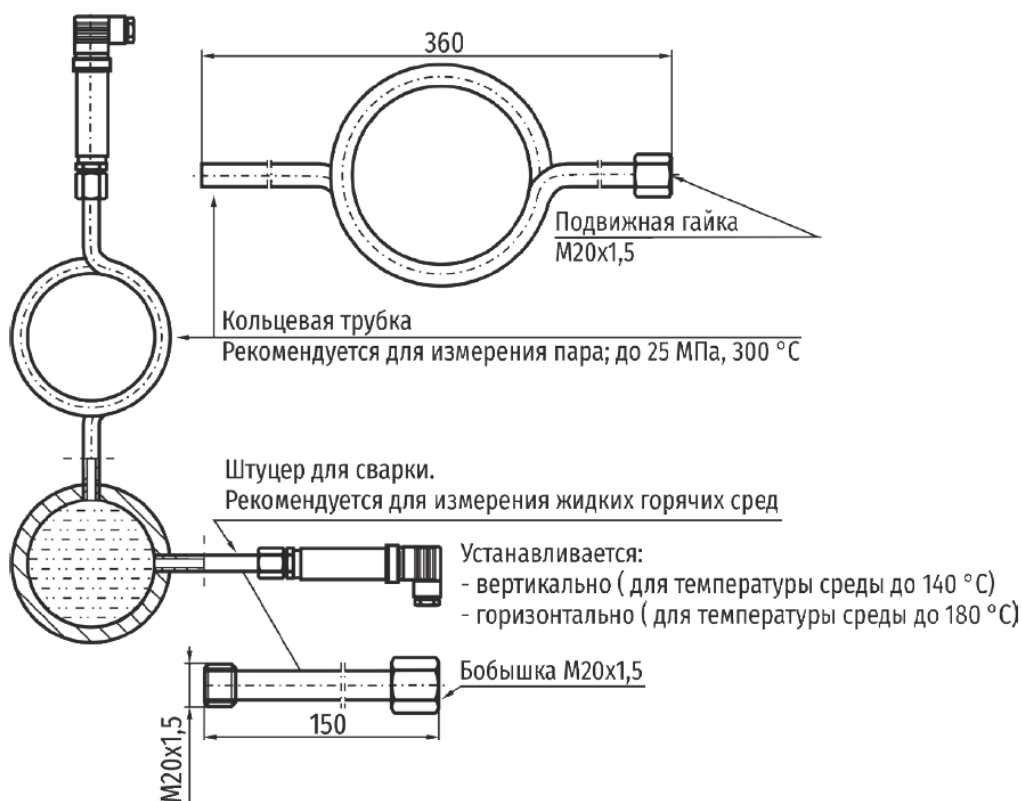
Примеры использования трубки кольцевой и штуцера для сварки с преобразователем давления РС-28 для измерения горячих сред
